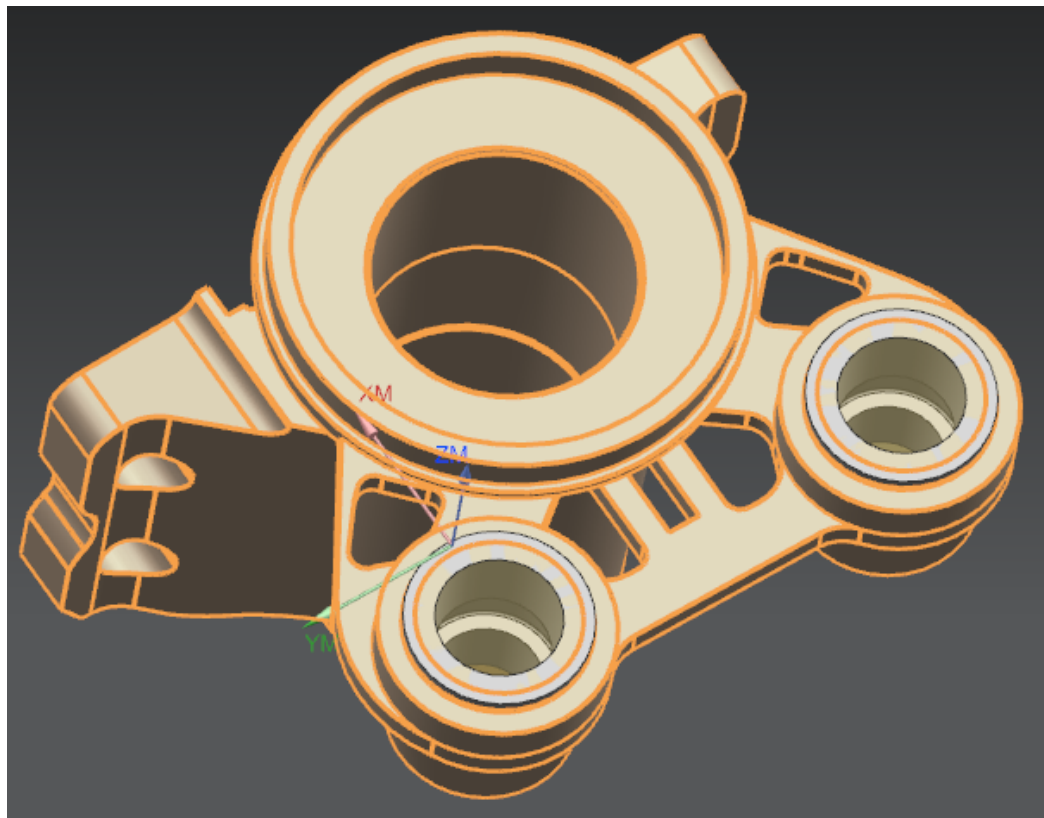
Совмещение поверхности детали и заготовки
